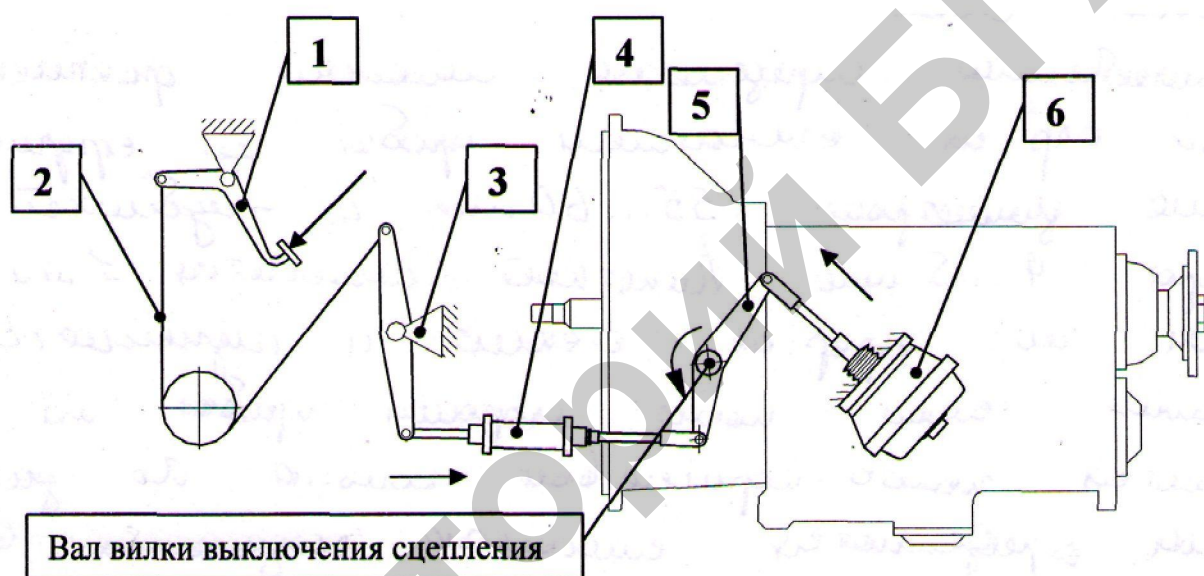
Схема привода управления двухдисковым сцеплением:
